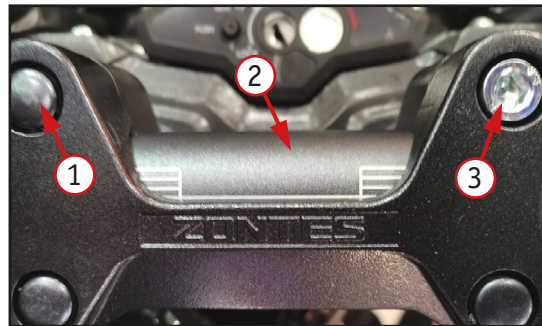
Крепление руля: 1 – пластиковые заглушки (4 штуки); 2 – руль; 3 – крепежные болты (4 штуки).
